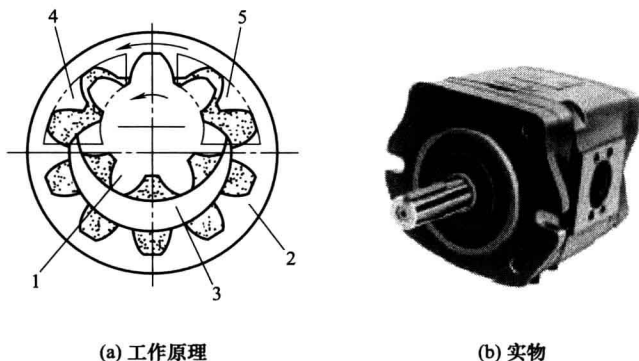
内啮合渐开线齿轮泵工作原理及实物
